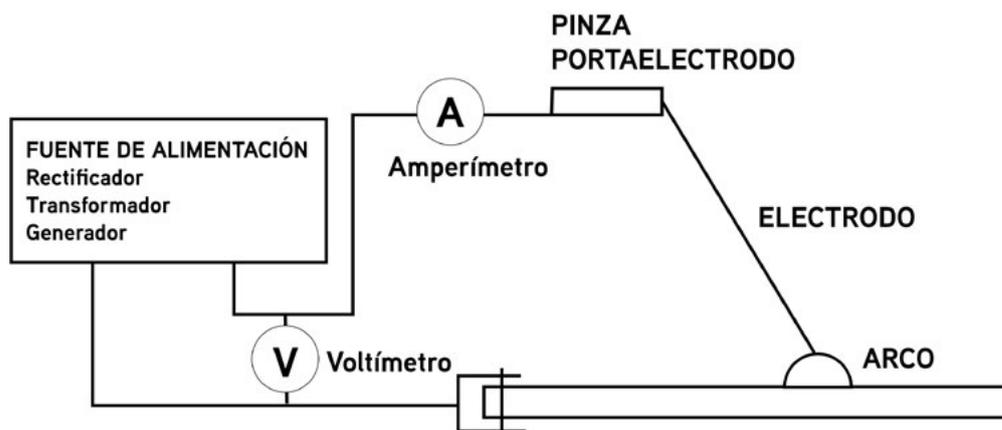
Esquema de procedimiento de soldadura con electrodo revestido
